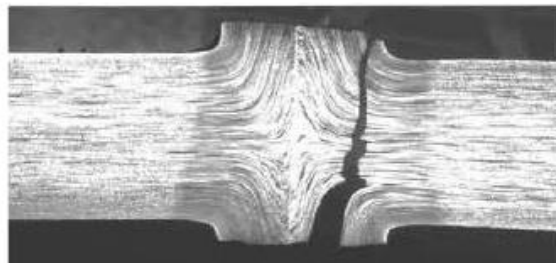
Cross section de un Hook crack de un caño que fallo en servicio
